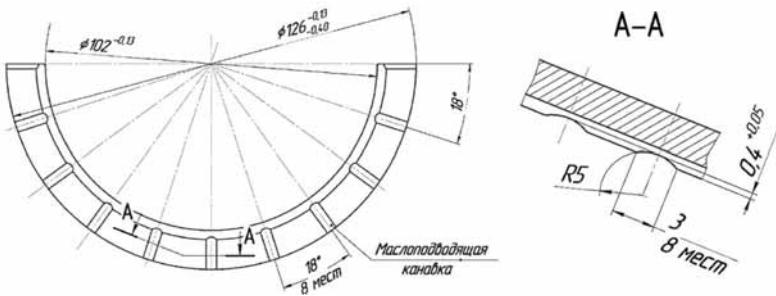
Упорное полукольцо с маслоподводящими канавками с криволинейными профилями
